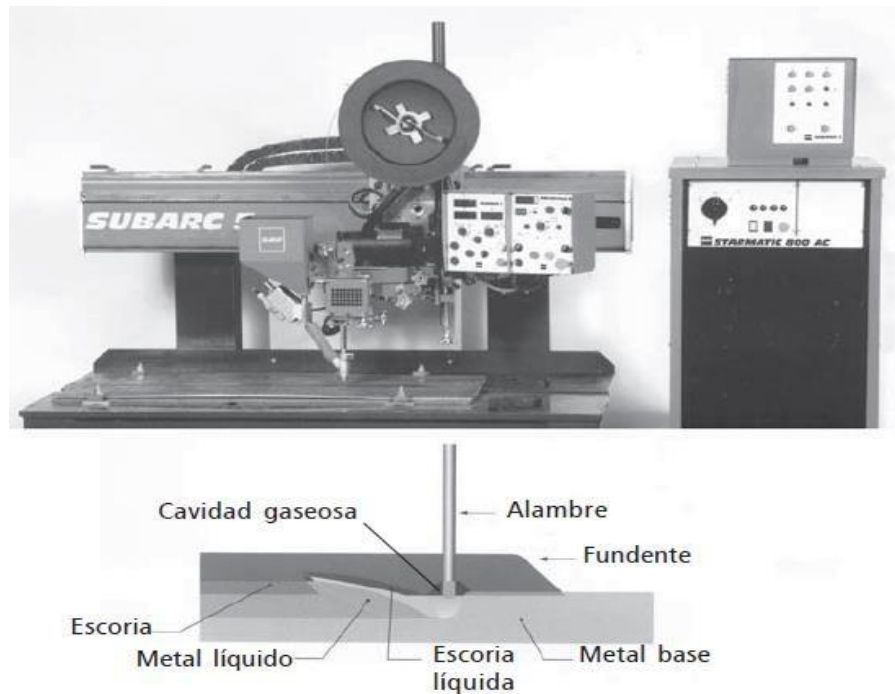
Proceso de soldadura por arco sumergido y equipo para soldadura por arco sumergido. Fuente: Manual de soldadura OERLIKON.
